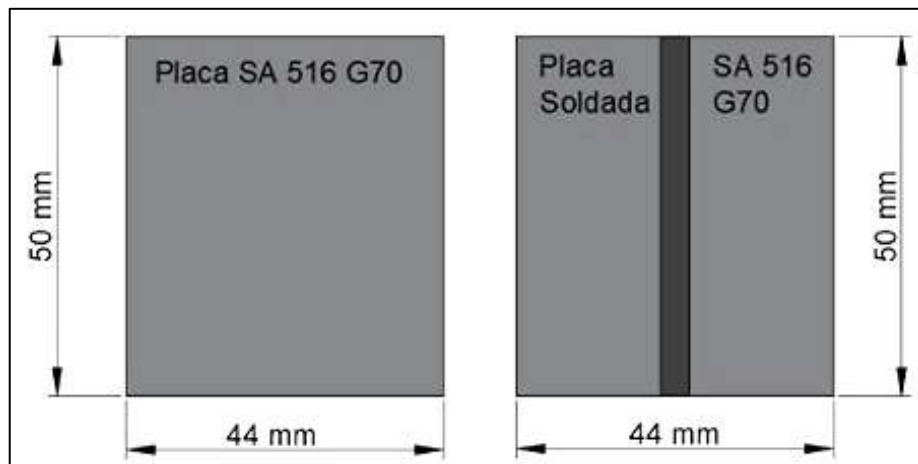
Dimensiones placas y juntas soldadas de acero SA-516 grado 70
